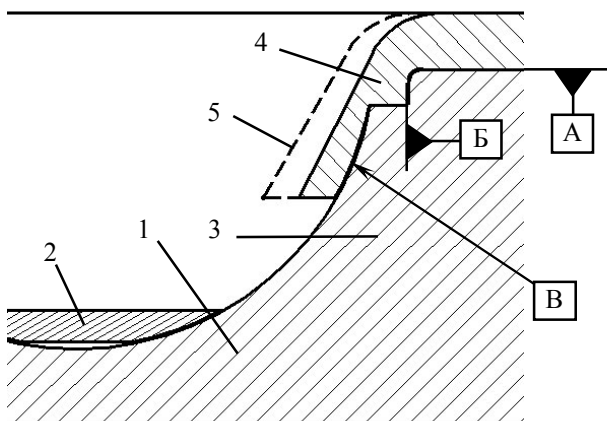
Схема установки и доработки малого конуса оснастки для перехода № 4: 1 – матрица; 2 – нижняя донная вставка; 3 – центральный выступ матрицы; 4 – малый конус; 5 – предварительная форма малого конуса; А и Б – базовые поверхности матрицы и вставок; В – вспомогательная база
